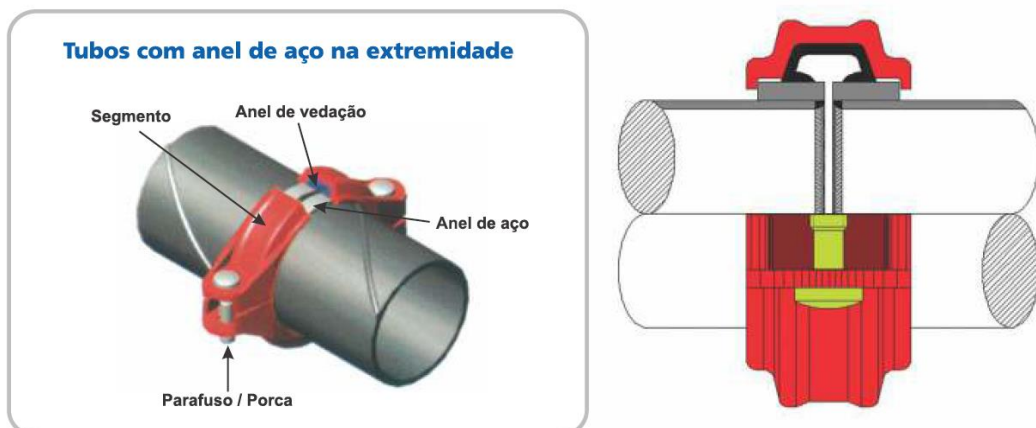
Tubo com anel de aço soldado a extremidade.
